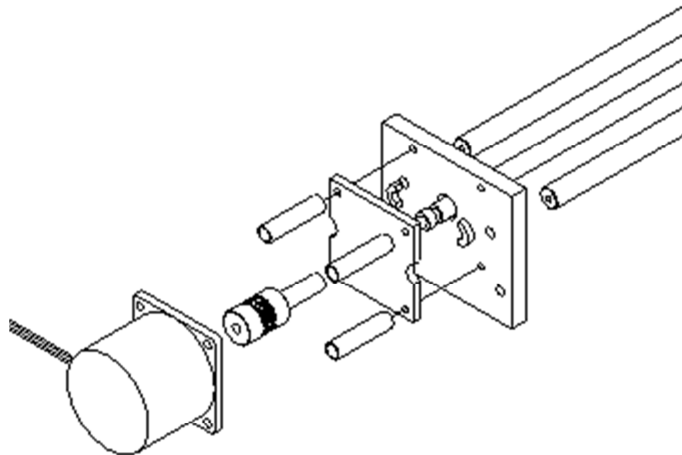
Ensamble de motor, acople y tornillo de posicionamiento
